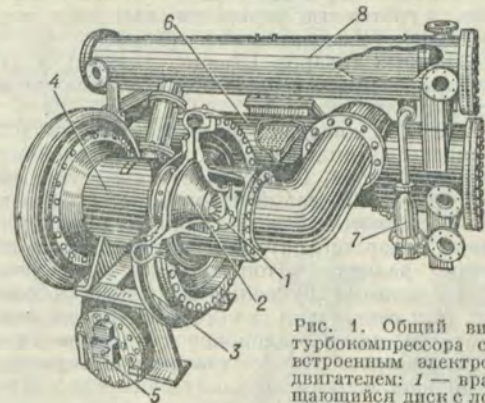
Общий вид турбокомпрессора со встроенным электродвигателем; 1 — вращающийся диск с лопатками; 2 — рабочее колесо 1-й ступени; 3 — корпус колеса; 4 — электродвигатель; 5 — приемный танк для масла; 6 — испаритель; 7 — поплавковый вентиль; 8 — конденсатор.
